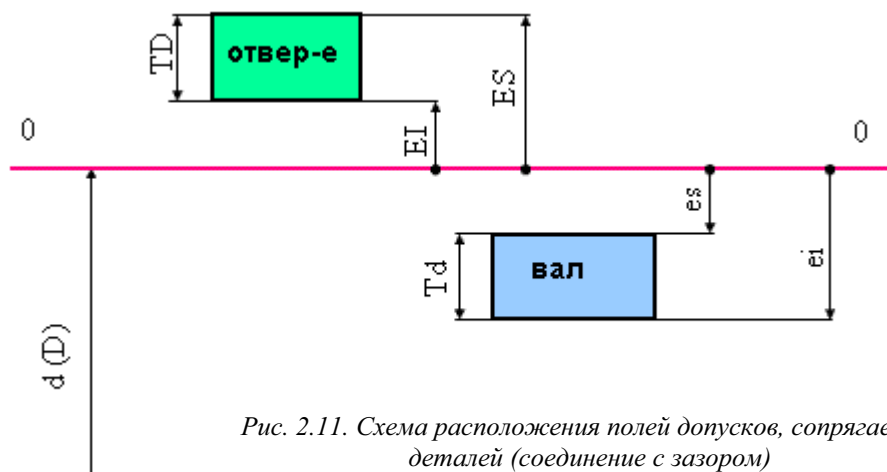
Схема расположения полей допусков, сопрягаемых деталей (соединение с зазором)
